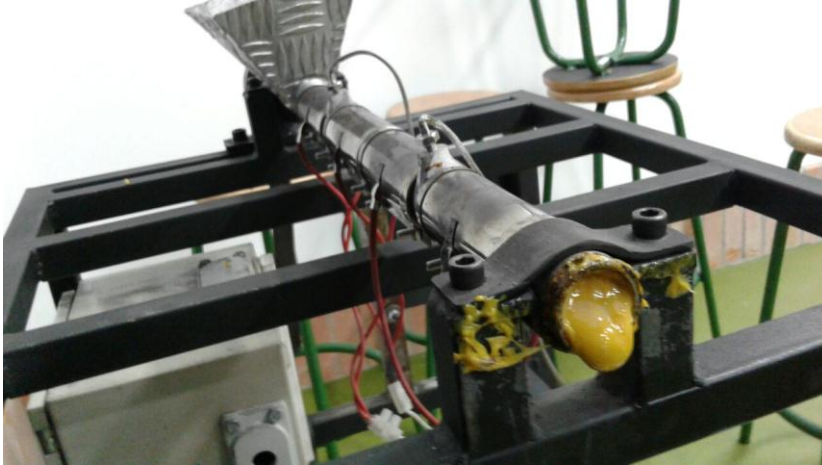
Calentamiento de extrusora para polímeros PET y de molde para uniones mediante soplete
